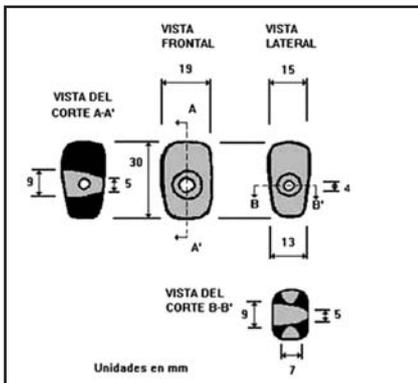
Principales cortes, vistas y dimensiones del generador de ruido bucal de ilmenita.
